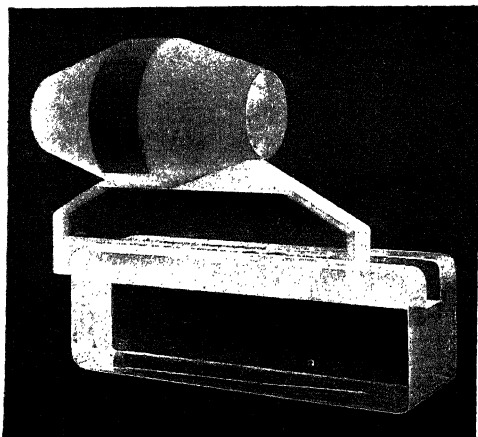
Mit Hartmetallwerkzeugen gefräste und gedrehte Glasstücke.
